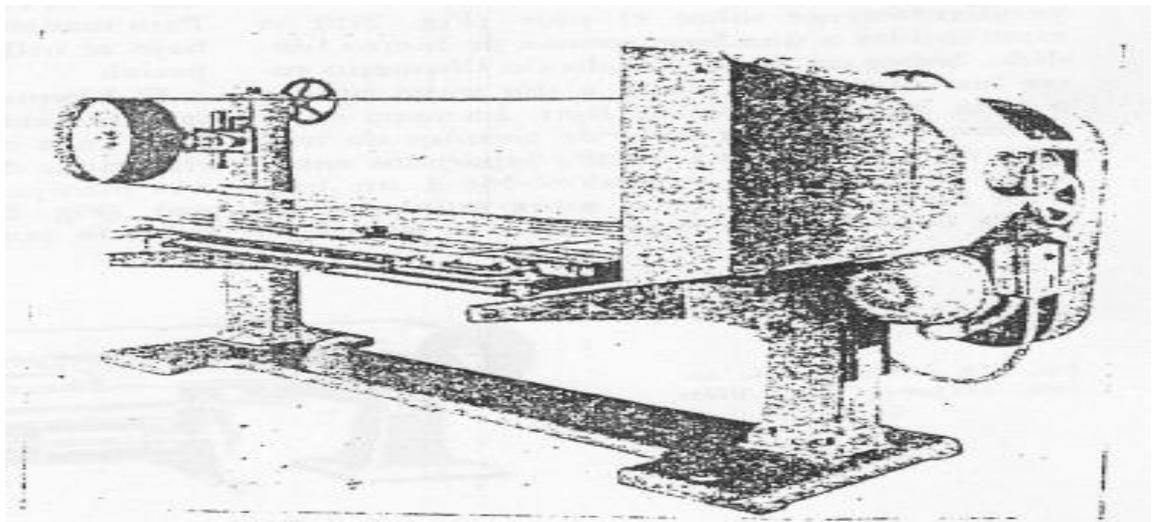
Lijadora de correa reversible impulsada a motor (Oliver Machinery Co.)
